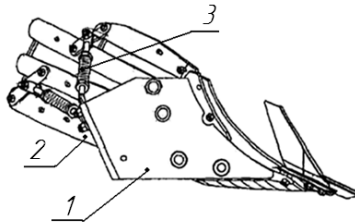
Патент RU 97234 «Рабочий орган почвообрабатывающего орудия»:
